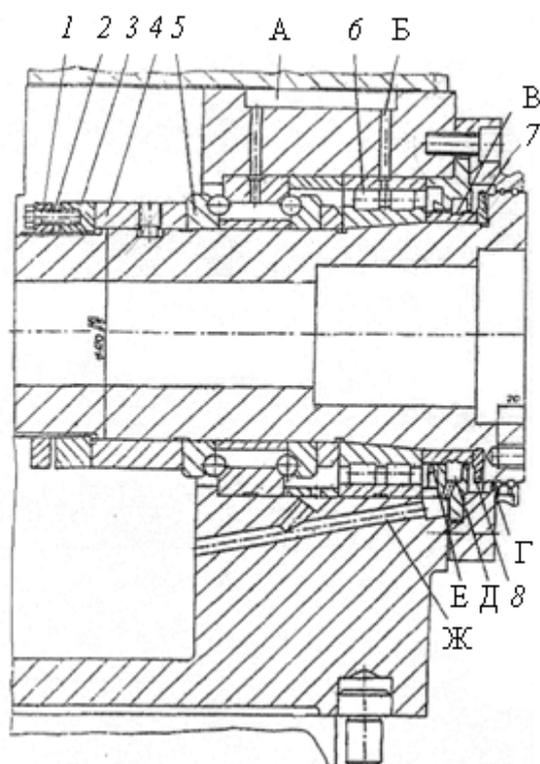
Передняя опора и конец шпинделя многоцелевого фрезерно-сверлильно-расточного станка
